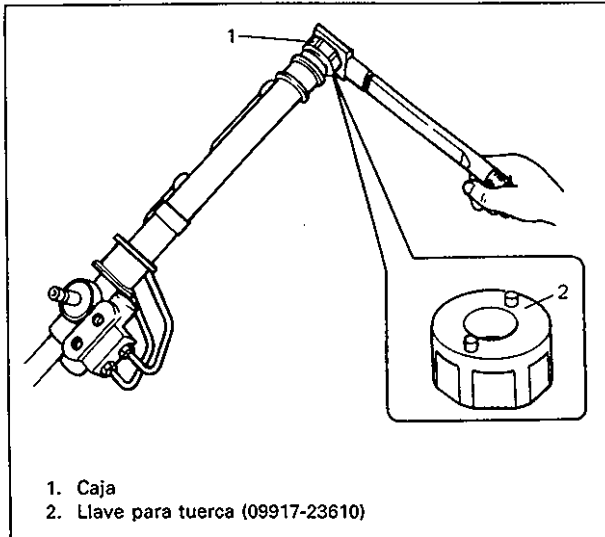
B1-39 Desmontaje de la caja del mecanismo de dirección
